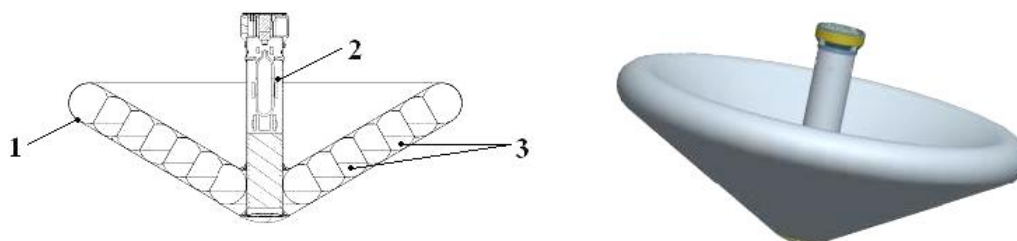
Схема перетворюваного спускового апарату [2]: 1 - захисна оболонка з кевлара; 2 - жорстка центральна частина конструкції із системою наддуву; 3 - тороїдальні несучі пневмобалони; загальний вигляд апарата (праворуч)
